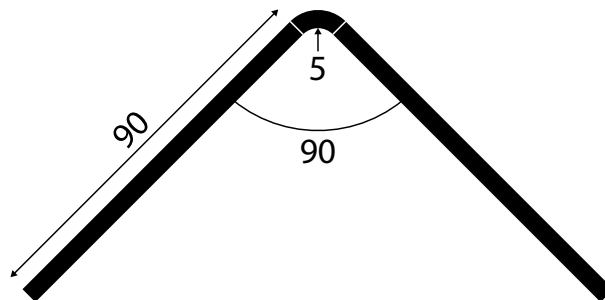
Géométrie de l'éprouvette en L (dimensions en millimètres, angle en degrés)
